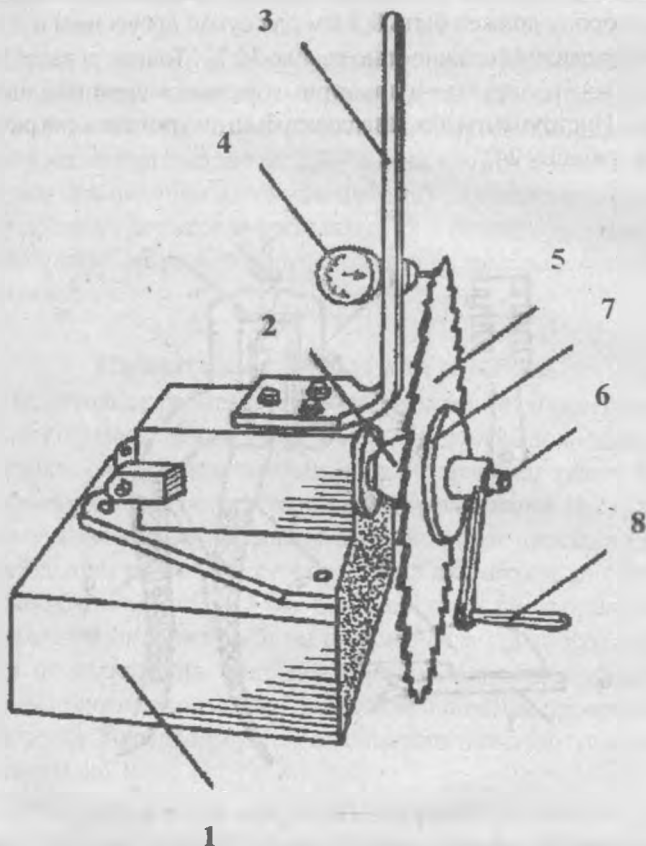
Приспособление для проверки качества правки круглой пилы:
